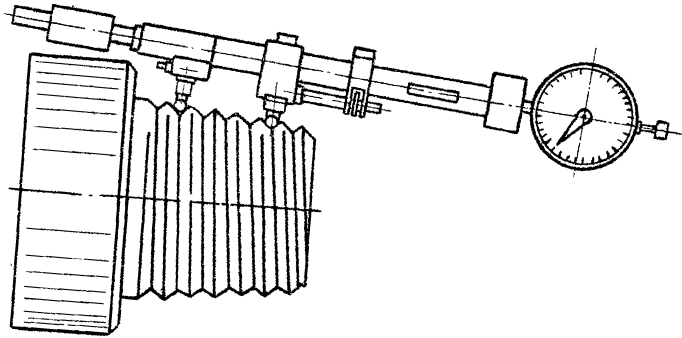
Проверка шага резьбы шагомером "ШИ".
